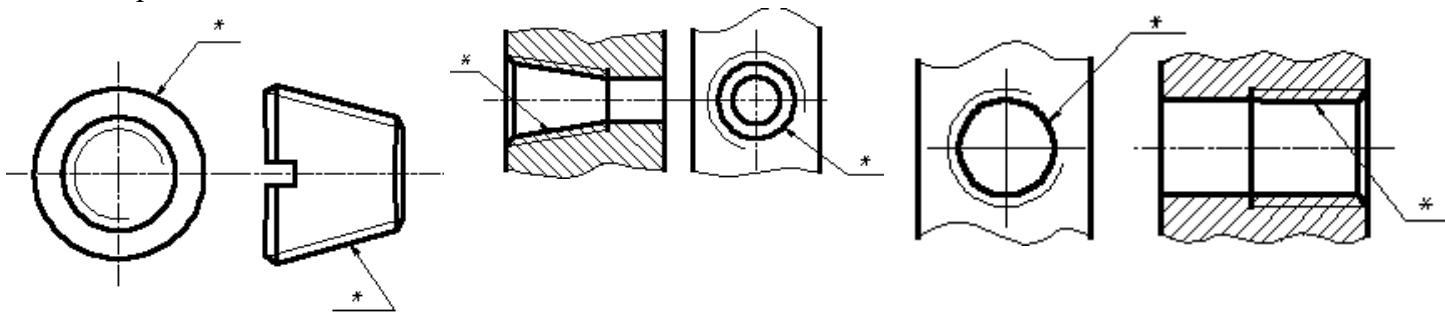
Пример обозначения конической и трубной цилиндрической резьбы
